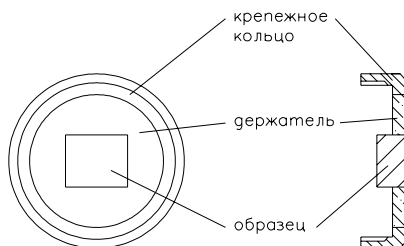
Кювета для крепления образца в гониометрической приставке ГП-4
